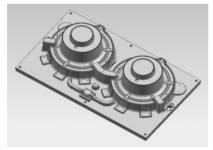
商用车制动盘下型模型三维图 Fig.3 3D view of the lower model of the Commercial Vehicle brake disc
